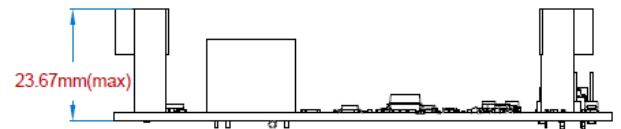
Dimensões mecânicas Flexcard I/O (PR17036)
